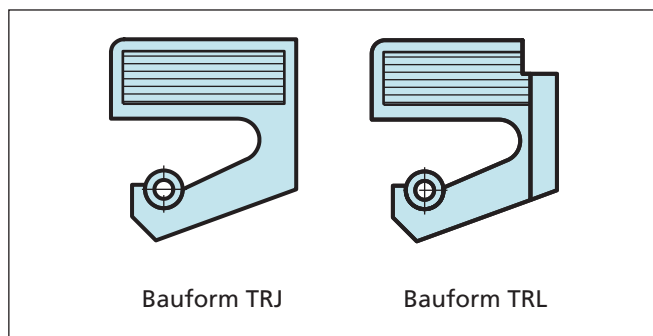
Gewebeverstärkte Ausführungen für große Durchmesser
